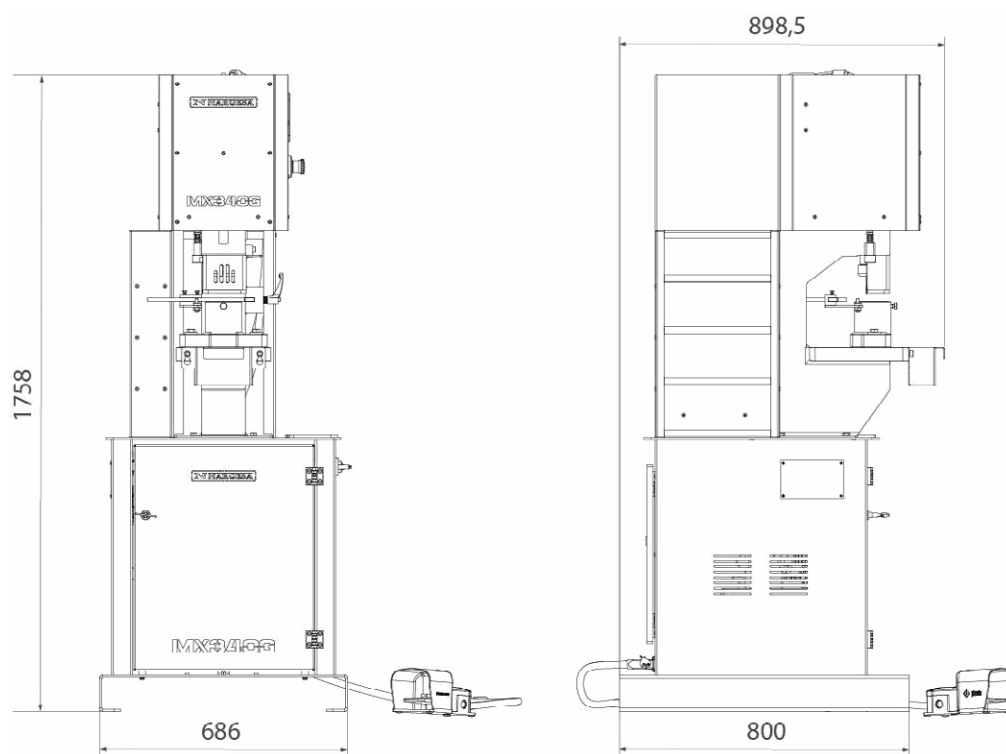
Dimensions extérieures de la poinçonneuse MX340G CNC
